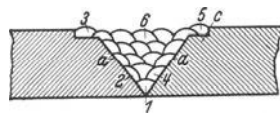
Anordnung der Lagen bei Gußeisenkaltschweißungen.
